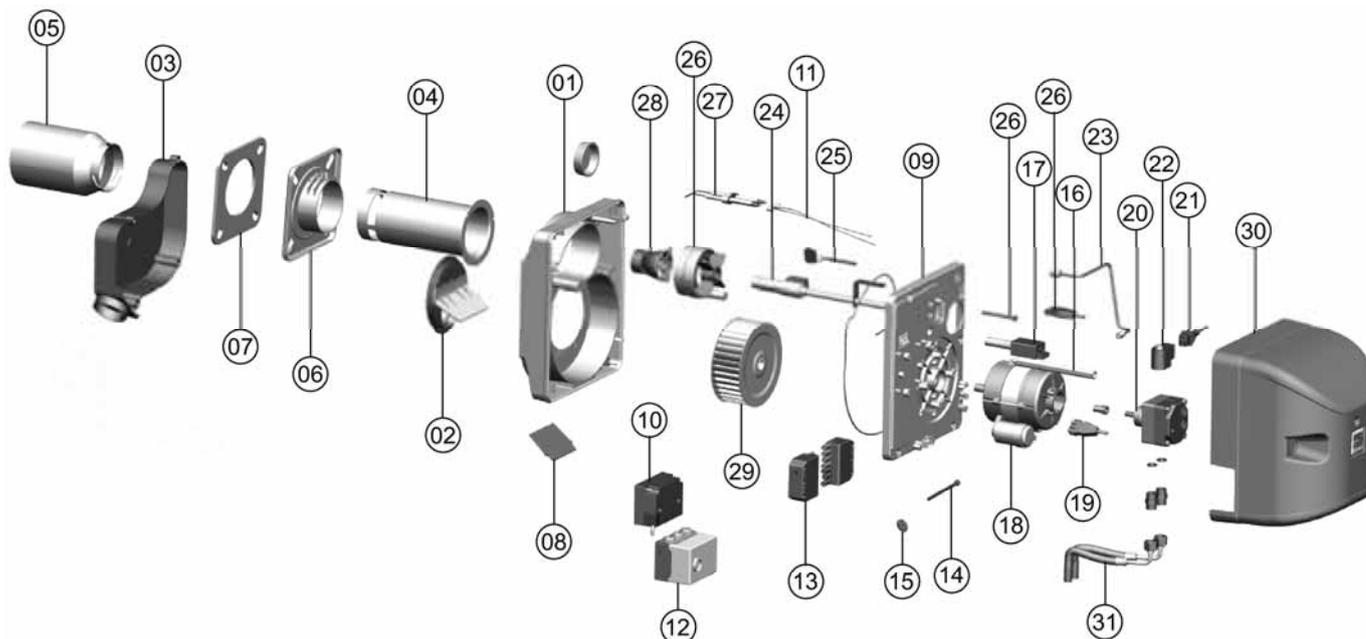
Explosionszeichnung BNR 100 / BNR 110
